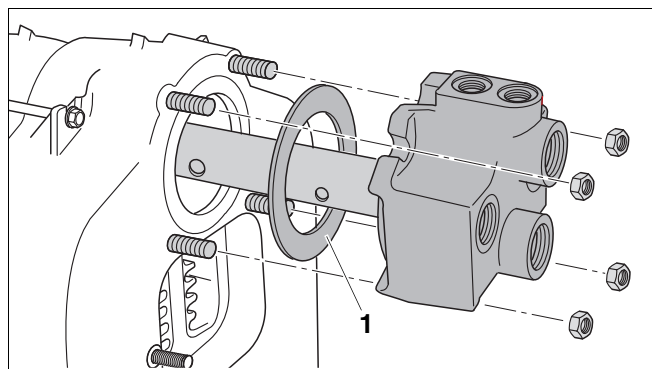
Montage du tube injecteur et de la pièce de raccordement spécifique
